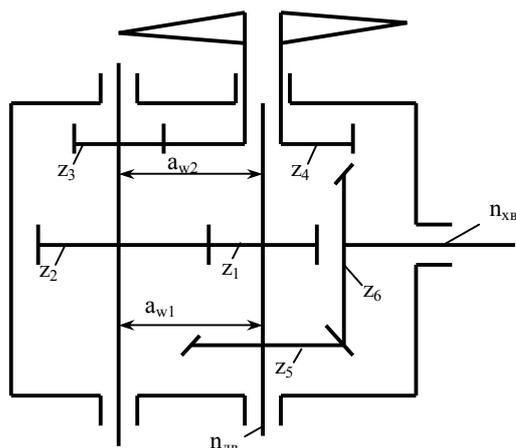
Кинематическая схема исследуемого главного редуктора вертолета
